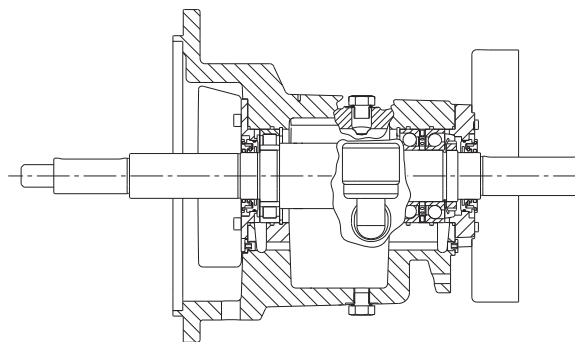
Корпус с роликовыми и двойными радиально-упорными подшипниками с масляной смазкой
